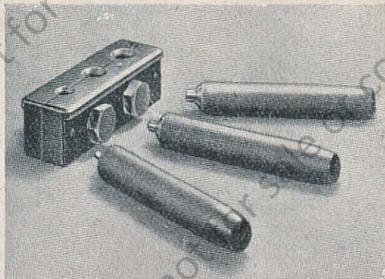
„Ate“-Bördelwerkzeug mit Dornen.
